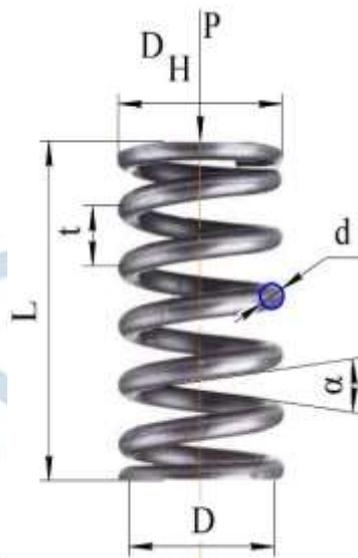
Конструкция стальной проволочной бытовой и цилиндрической пружины
